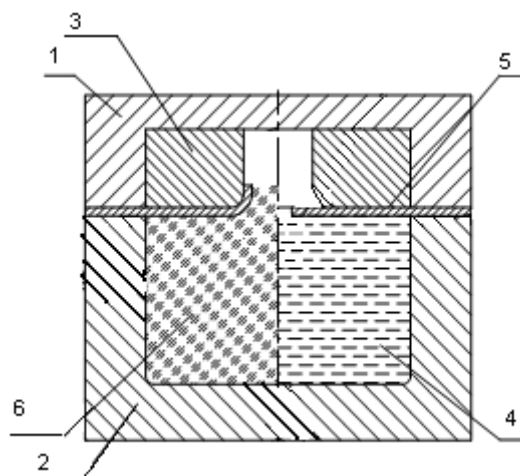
Устройство для отбортовки отверстий в листовой заготовке
